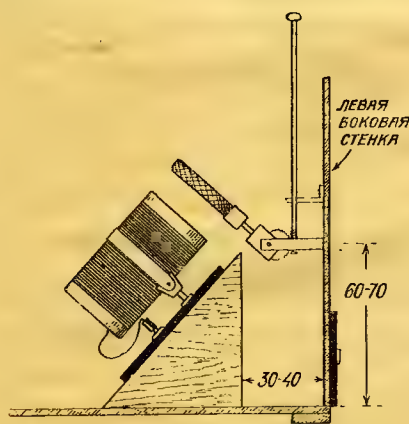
Крепление катушки L_1 и устройство подвижного станочка для катушки обратной связи.
